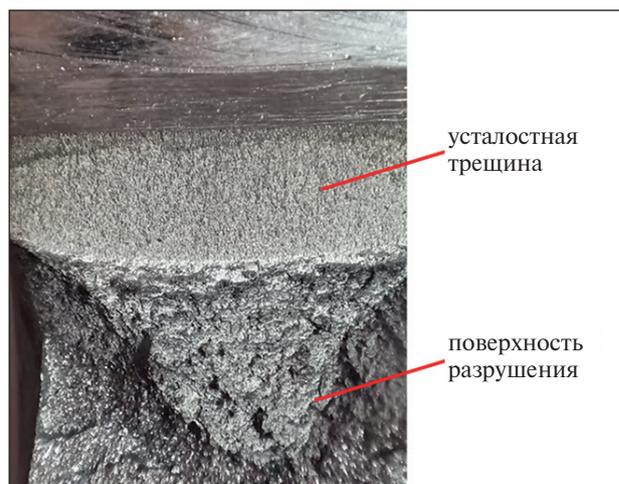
Поверхность образца с пророщенной трещиной, шероховатость которой измерялась профилометром TR200
